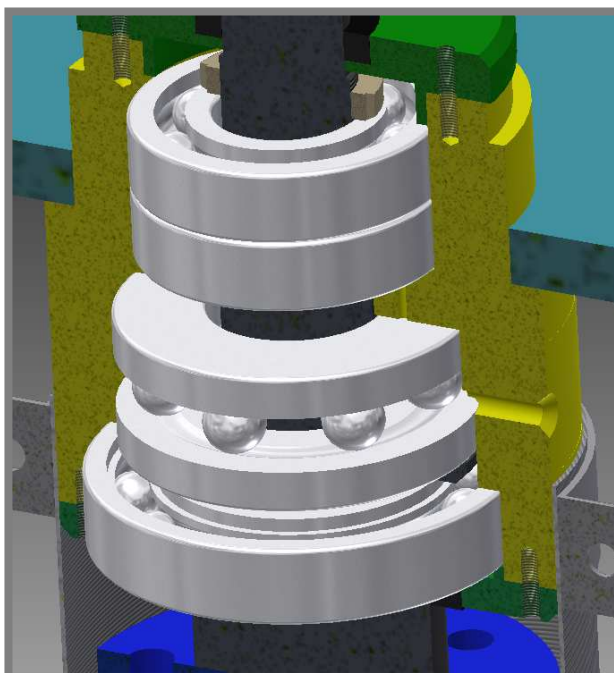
Detail konstrukčního řešení 4 (Vrchní část jímky)
